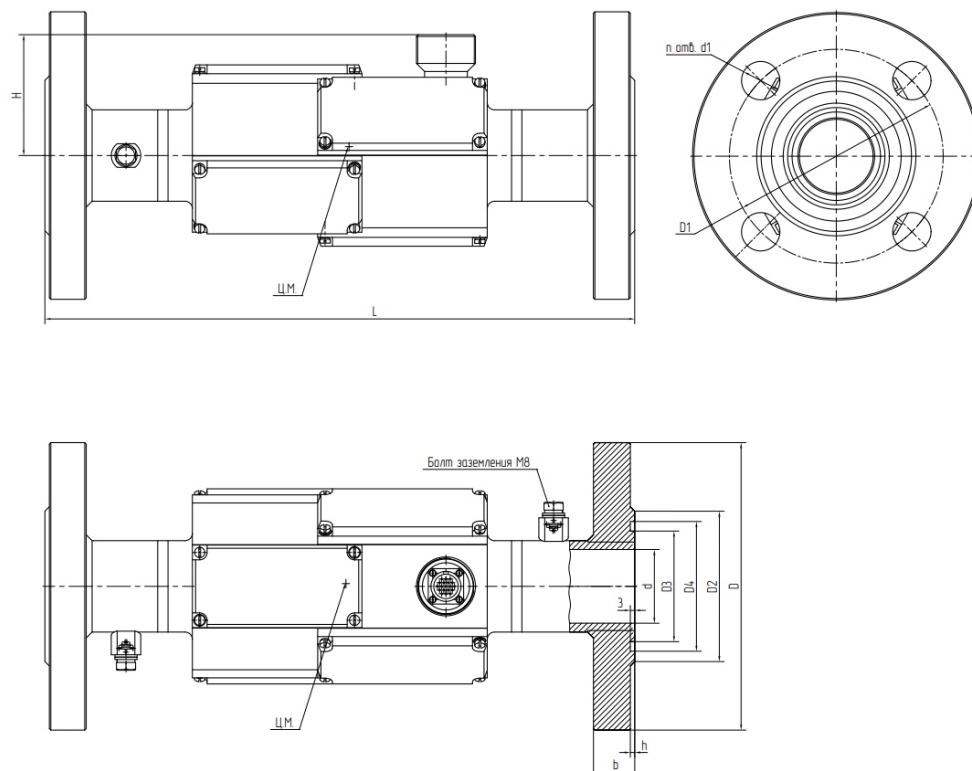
Габаритные и установочные размеры ПП с присоединением фланцем по ГОСТ 33259-2015
